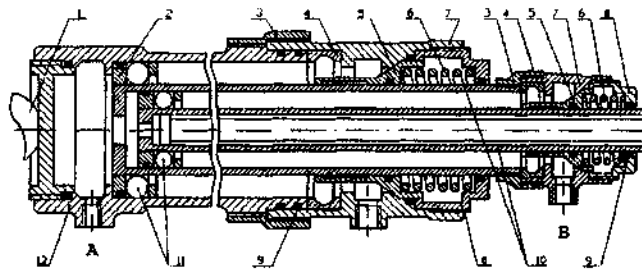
Силевой гидроцилиндр двустороннего действия: 1 — узел крепления гидроцилиндра; 2 — поршни; 3 — соединительные гайки; 4 — кольца замка; 5 — распорные цилиндры; 6 — пружины; 7 — запорные цилиндры; 8 — направляющие секции штока цилиндров; 9 — уплотнения; 10 — штоки поршней; 11 — шарики; 12 — корпус
